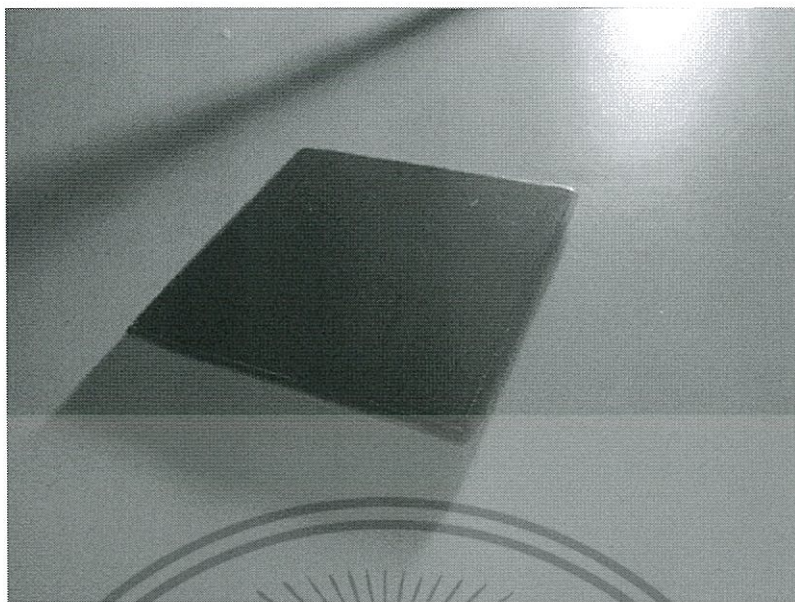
นำแผ่น PCB เข้าเครื่องรีด
